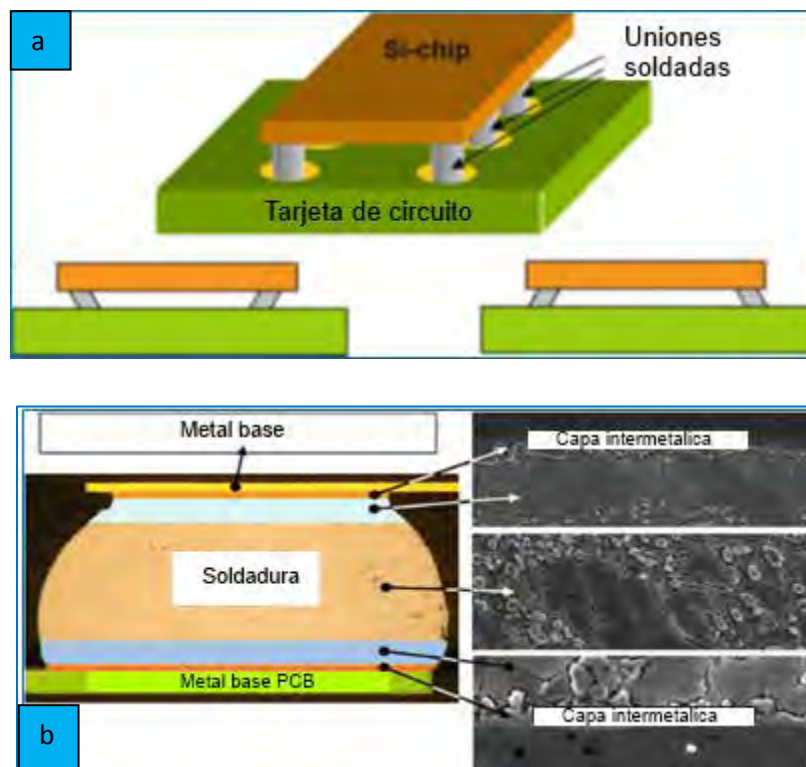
Esquema de la disposición de un componente electrónico a través de una soldadura sobre una PCB, b) las interacciones microestructurales generadas entre el componente electrónico-soldadura-PCB [7].
